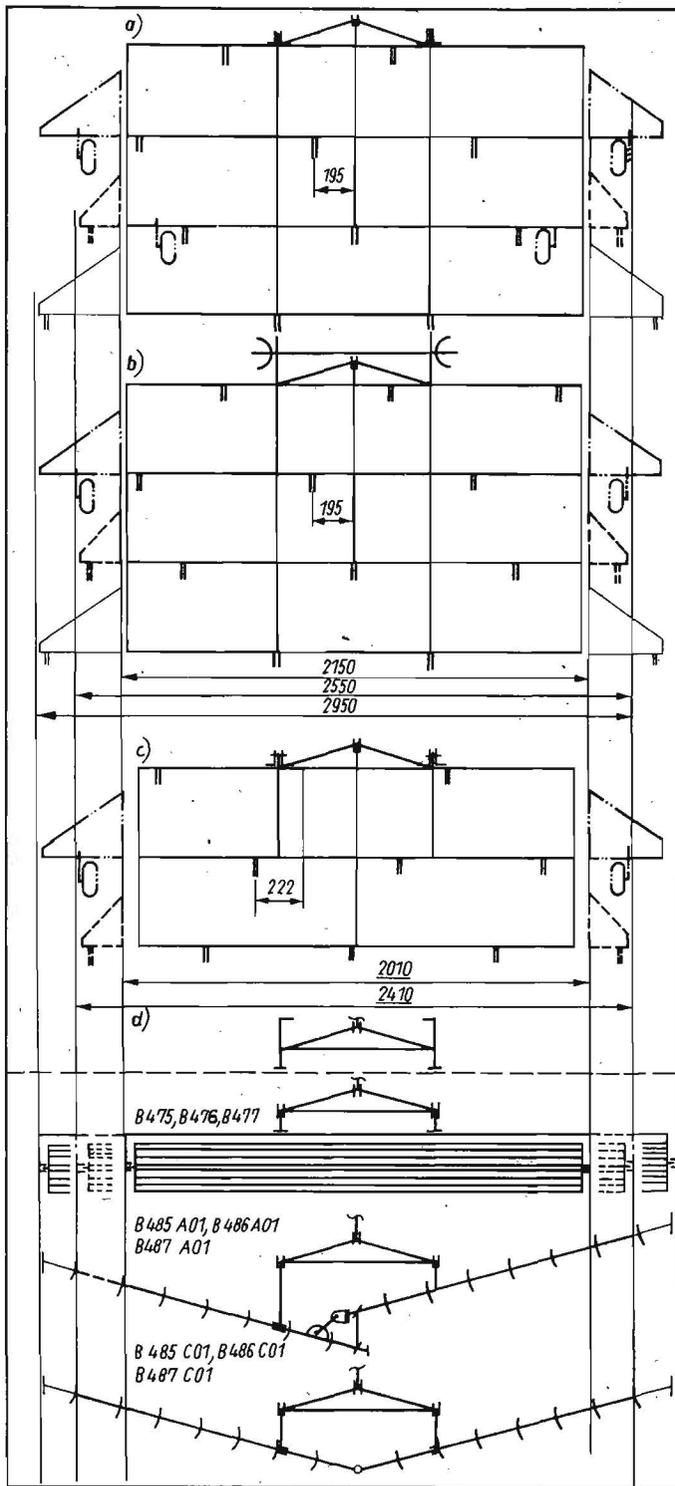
Anbauschema der Schwergrubber B 365 A, B 365 C und B 365 E mit Zusatzausrüstungen und Nachlaufgeräten;
